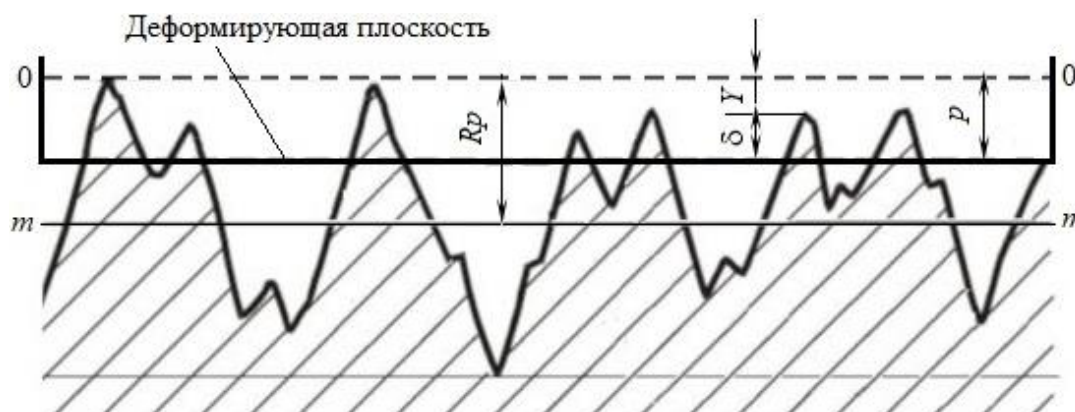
Схема контакта шероховатой поверхности с гладким плоским штампом: 00 – исходное положение штампа; mm – средняя линия профиля шероховатости
